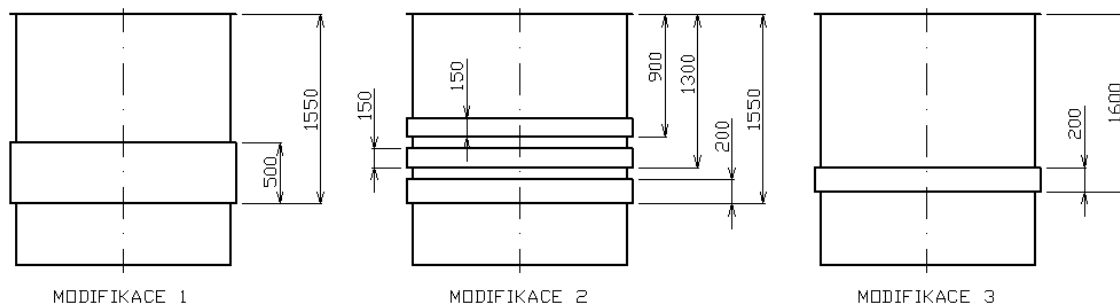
Rozmístění pásů pro základní tloušťku stěny 8 mm
